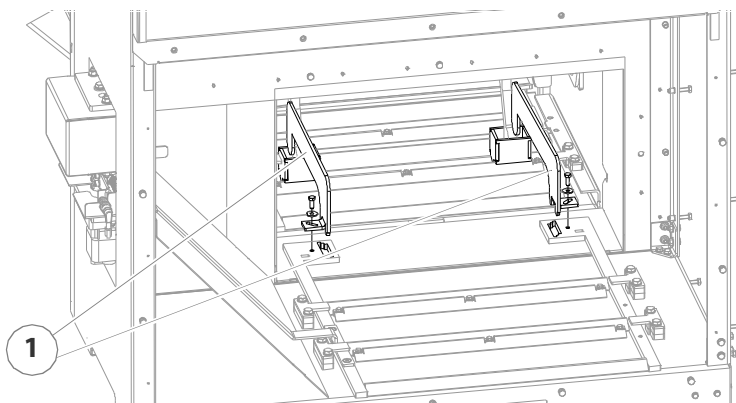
/42 - Raccordement du plancher poussant pour les cendres
